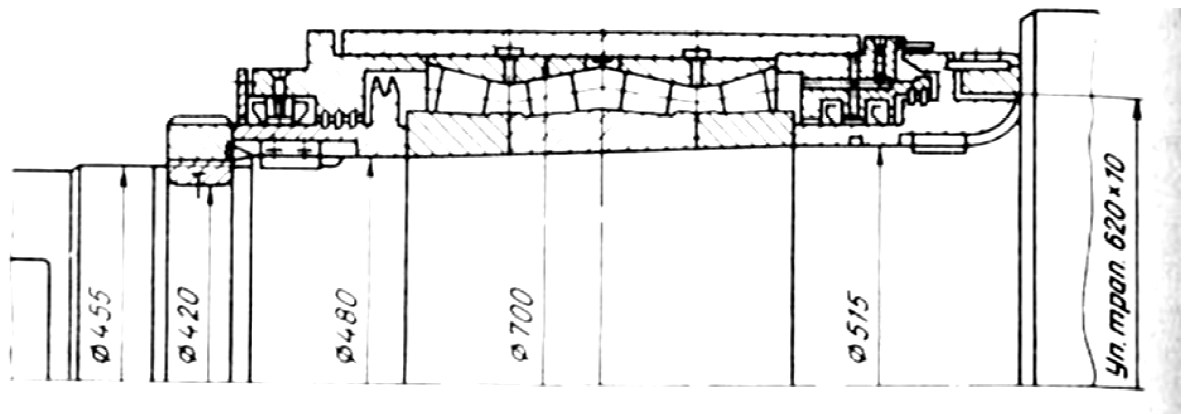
Установка рабочего валка с конической шейкой чотирьох валкового стани 2000 на роликових конічних підшипниках
